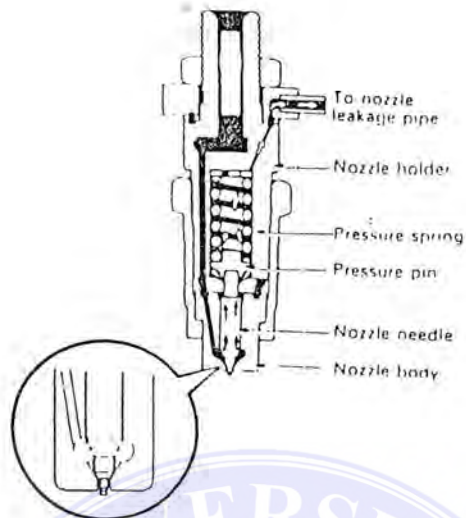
Pengeinjeksian Bahan Bakar.
